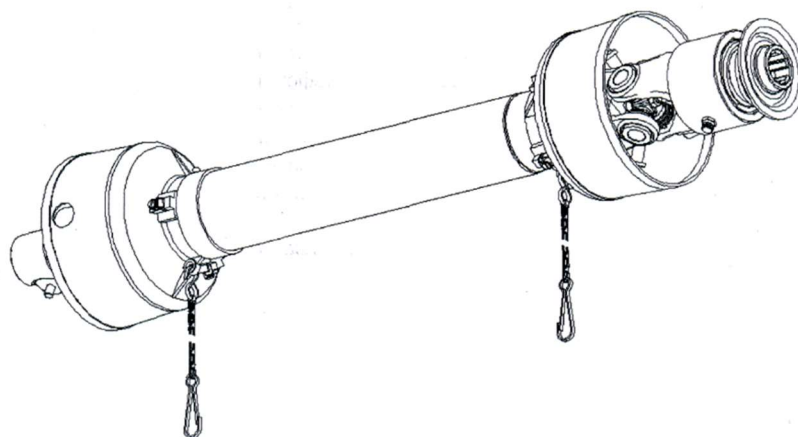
Конструкция карданного вала АК-40.016.3000-065/098
